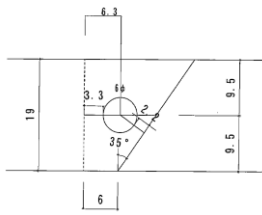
溶接部試験片位置 写真-2.3 試験片
